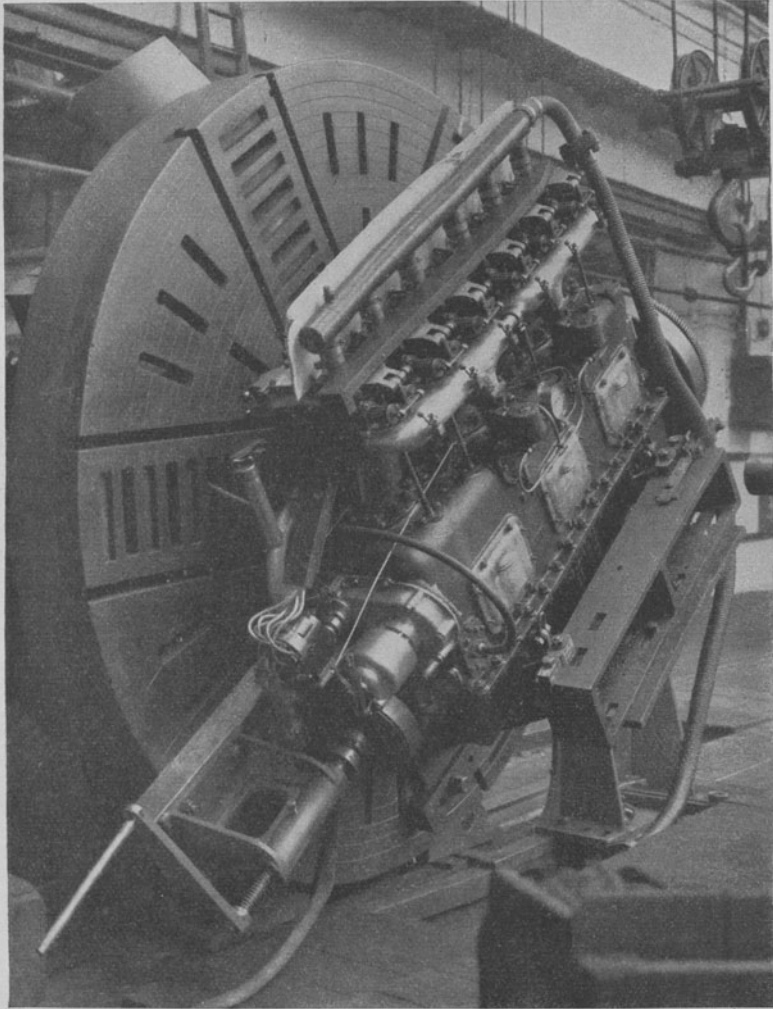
Maschine von 225 PS für Tanks. Aufbau für den Lauf in Schräglage.
